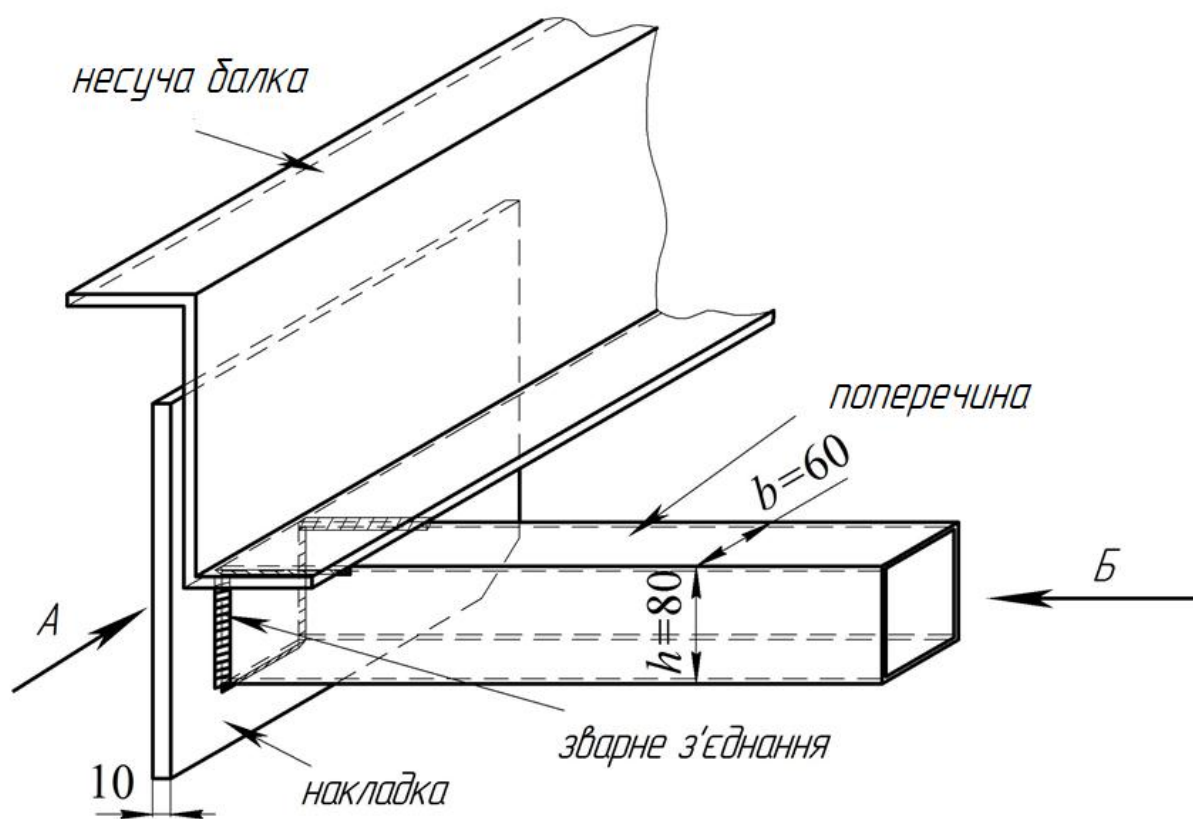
Зварне з'єднання поперечини з несучою балкою
